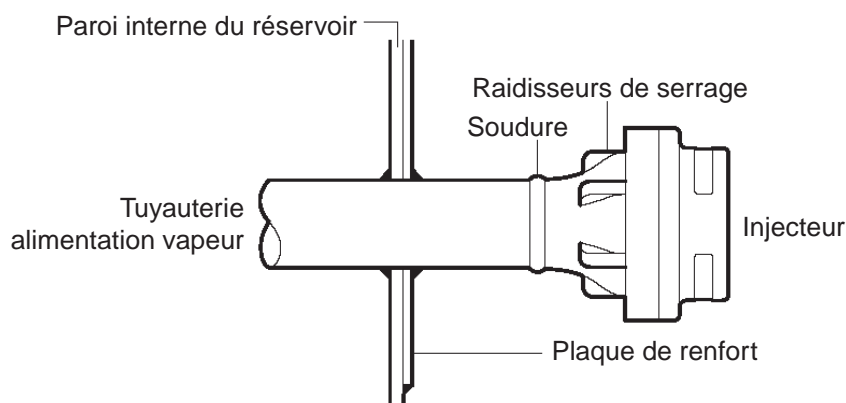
IN25M/IN40M - A souder BW - Installation typique sur une paroi du réservoir (sur tube soudé)
